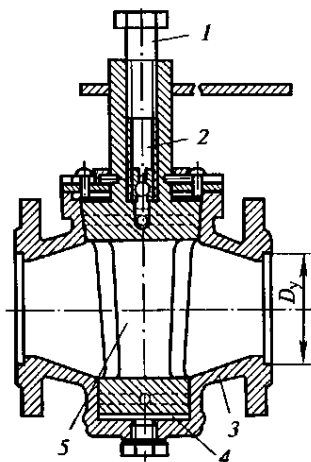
Кран чугунный со смазкой типа КС и ручным управлением:
